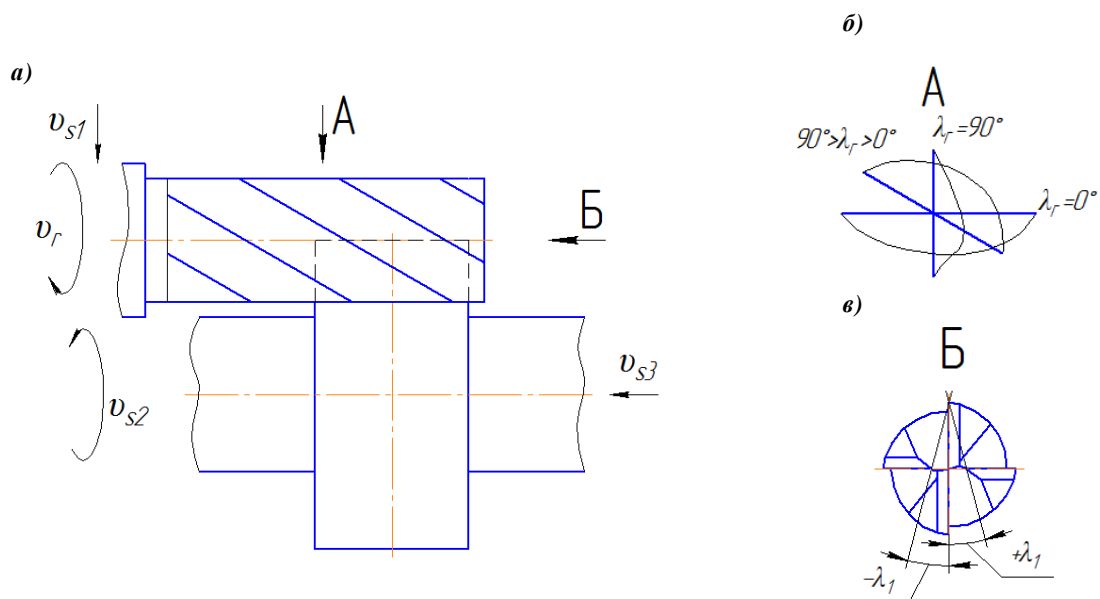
Схема обработки плоской поверхности вращающейся детали вращающимся инструментом (а) и возможные углы наклона режущей кромки на цилиндрической (б) и торцевой (в) поверхностях концевой фрезы
